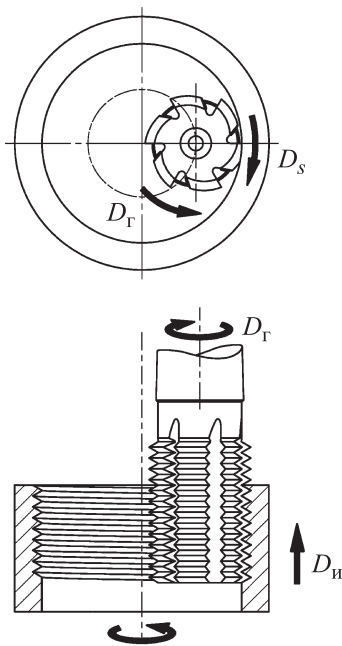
Кинематическая схема фрезерования внутренней резьбы гребенчатой фрезой
